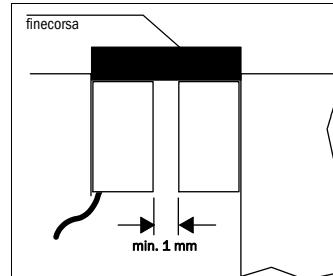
esempio di montaggio per un interruttore di sicurezza e un attuatore
